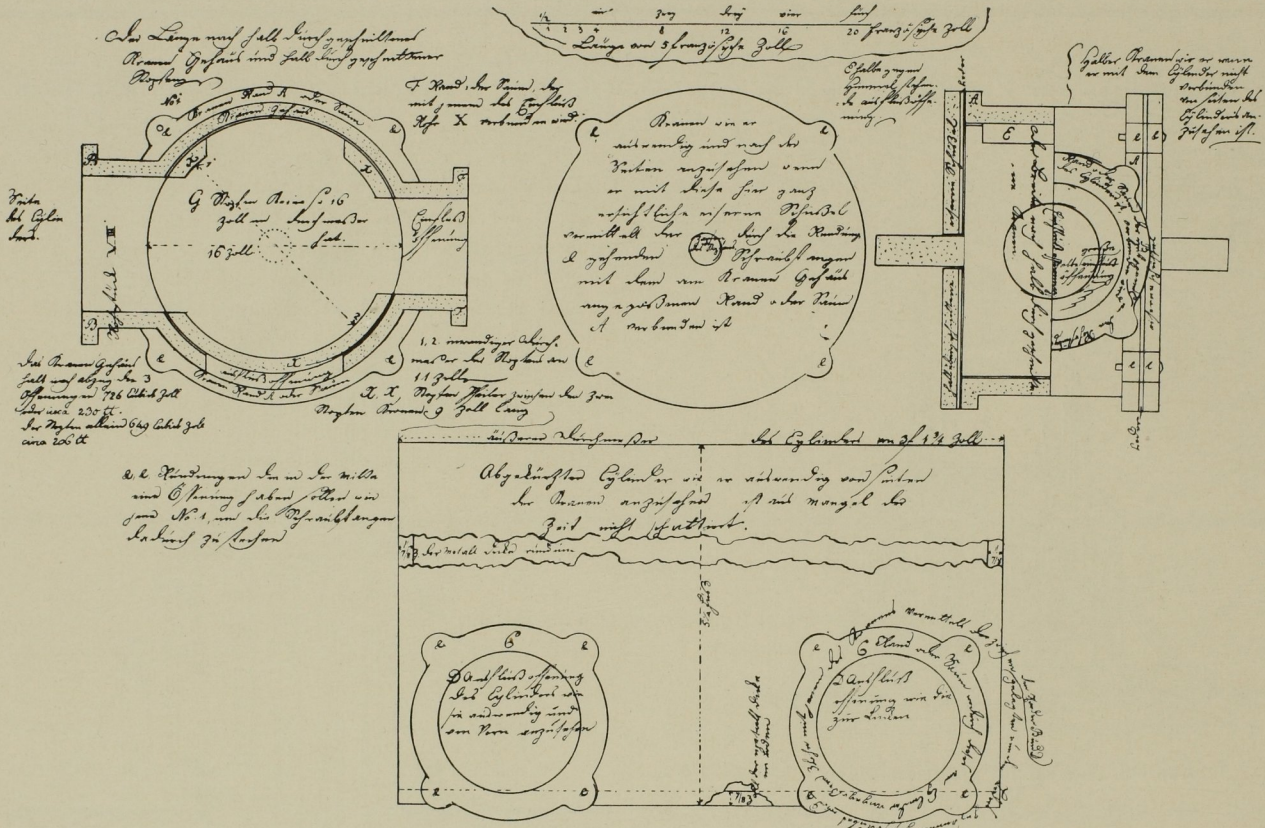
Werkzeichnung des Cylinders einer Wassersäulen-Maschine.
